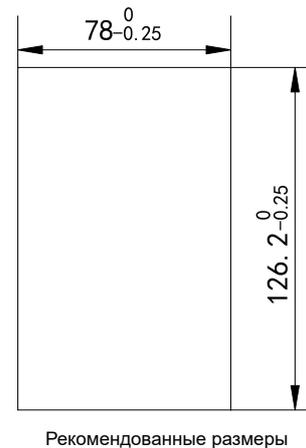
Чертеж установки опорной пластины (вырез в двери шкафа)
